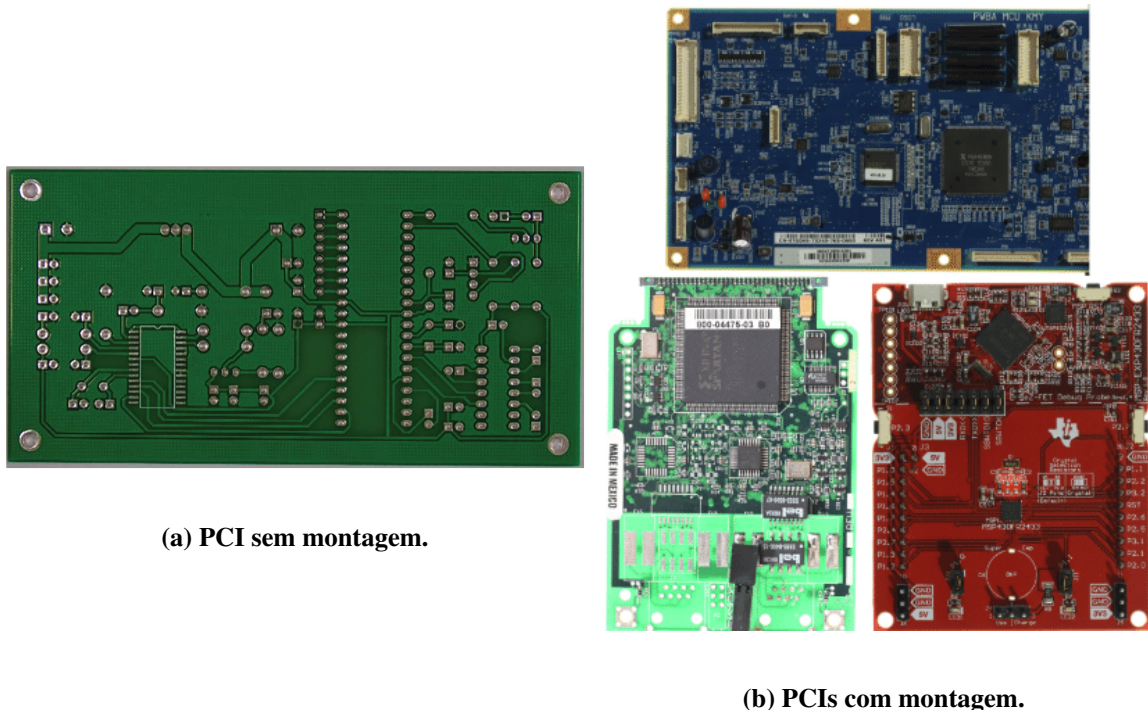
Exemplos de PCIs sem e com montagem. O que diferencia os dois tipos é a solda ou montagem dos componentes.
